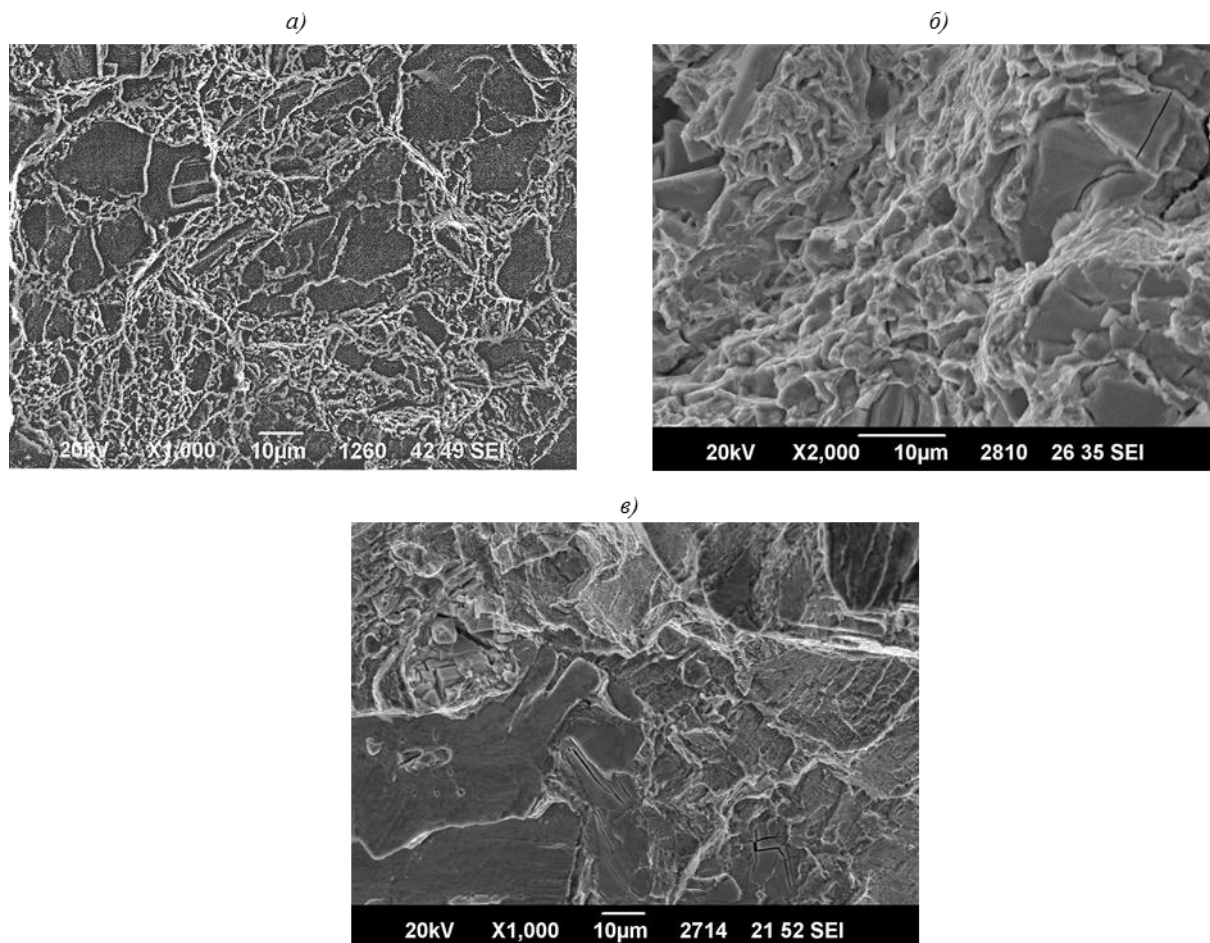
Фрактография изломов сварных соединений сплава ВЖ175
